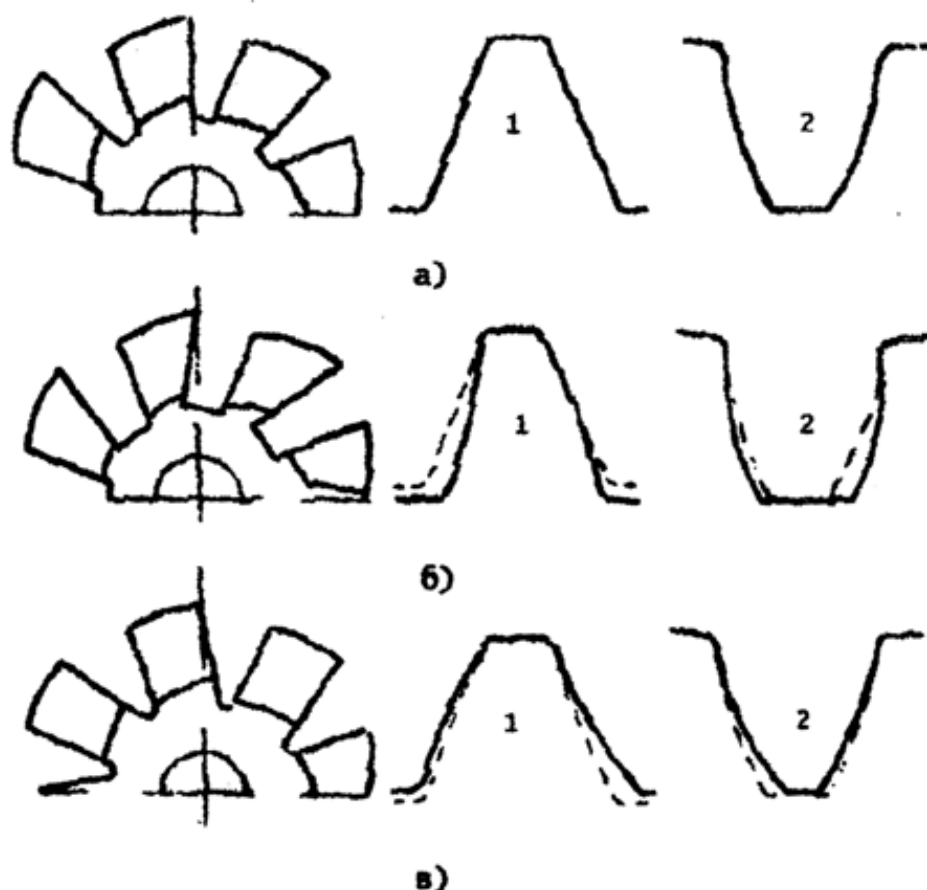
Влияние погрешностей точки червячной фрезы на профиль зубьев нарезного колеса:
